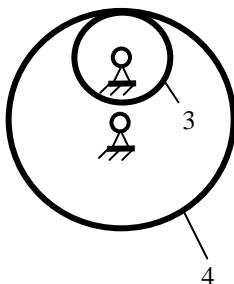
Зубчатая передача с внутренним зацеплением колёс
